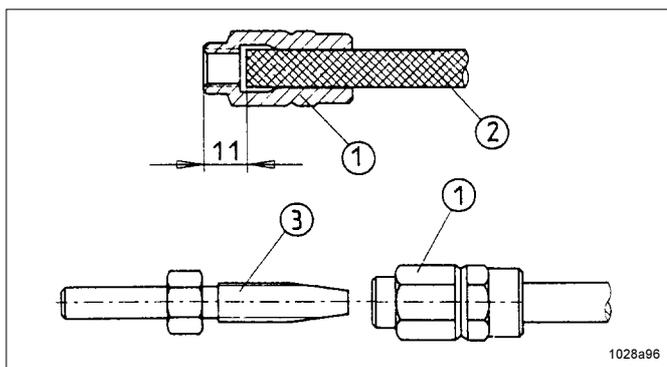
Prémontage des douilles filetées et des embouts pour tuyau sur la conduite principale
